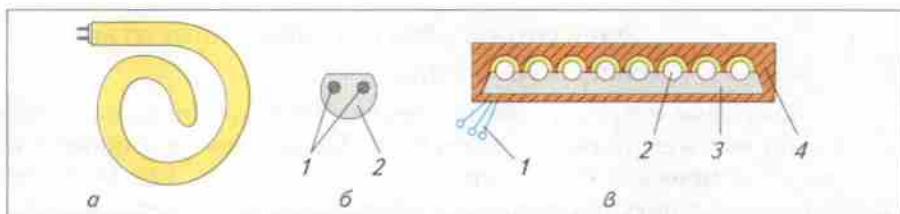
Герметизированный нагревательный элемент: *а* — трубчатый; *б* — вид трубчатого электронагревательного элемента со стороны цоколя (1 — выводы спирали, 2 — изолят); *в* — чугунная конфорка в разрезе (1 — контакты спирали, 2 — спираль, 3 — изоляционный материал, 4 — корпус конфорки)
